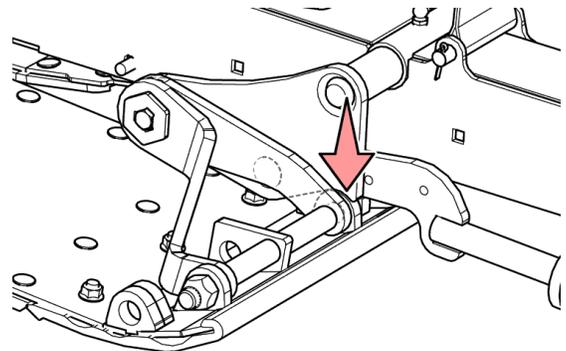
Punto de contacto de zapata deslizante de la pala final
